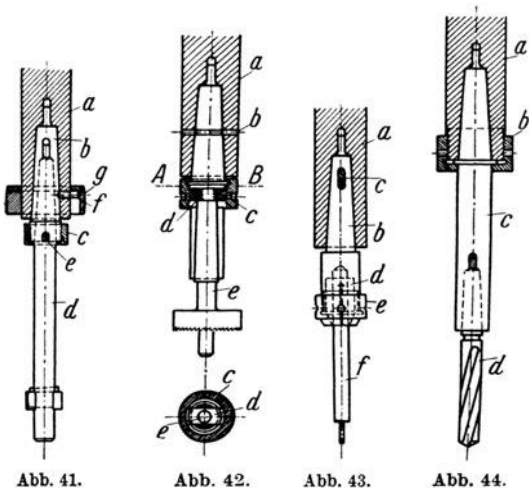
44. Spanneinrichtungen für Bohrmaschinenwerkzeuge.
